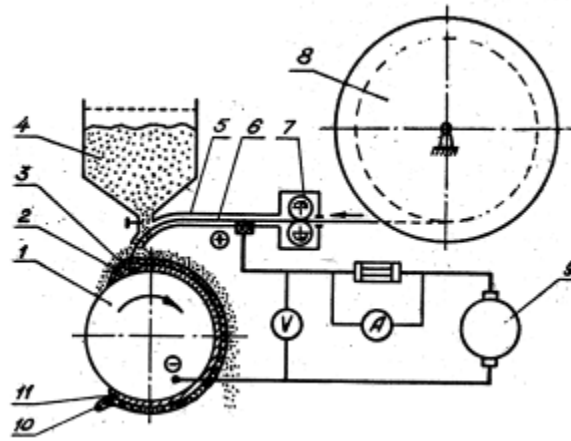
Схема автоматической наплавки под слоем флюса:
